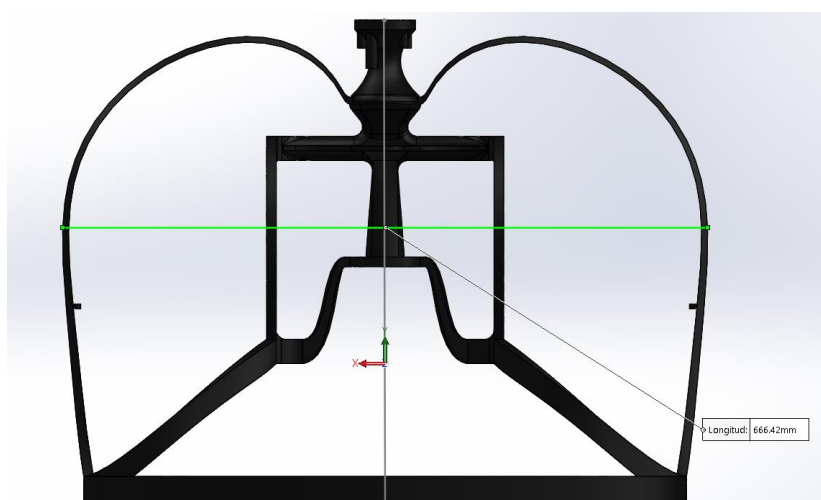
Dimensions cos utillatge; Font: Pròpia.
